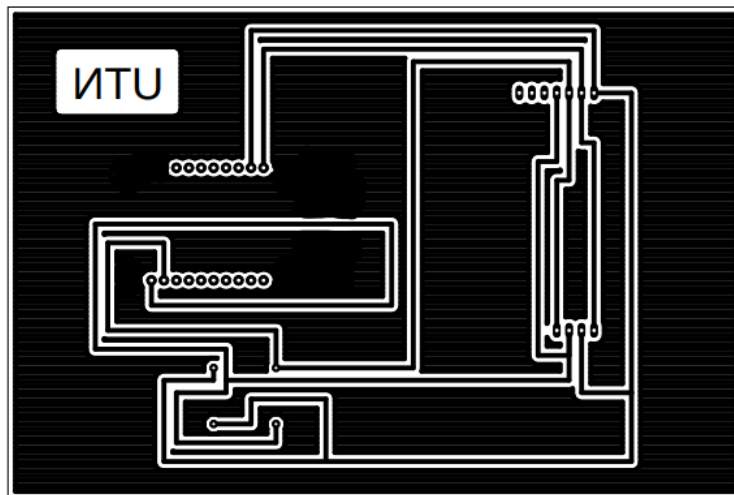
Diseño de la PCB - Shield para los nodos 1 y 2.
